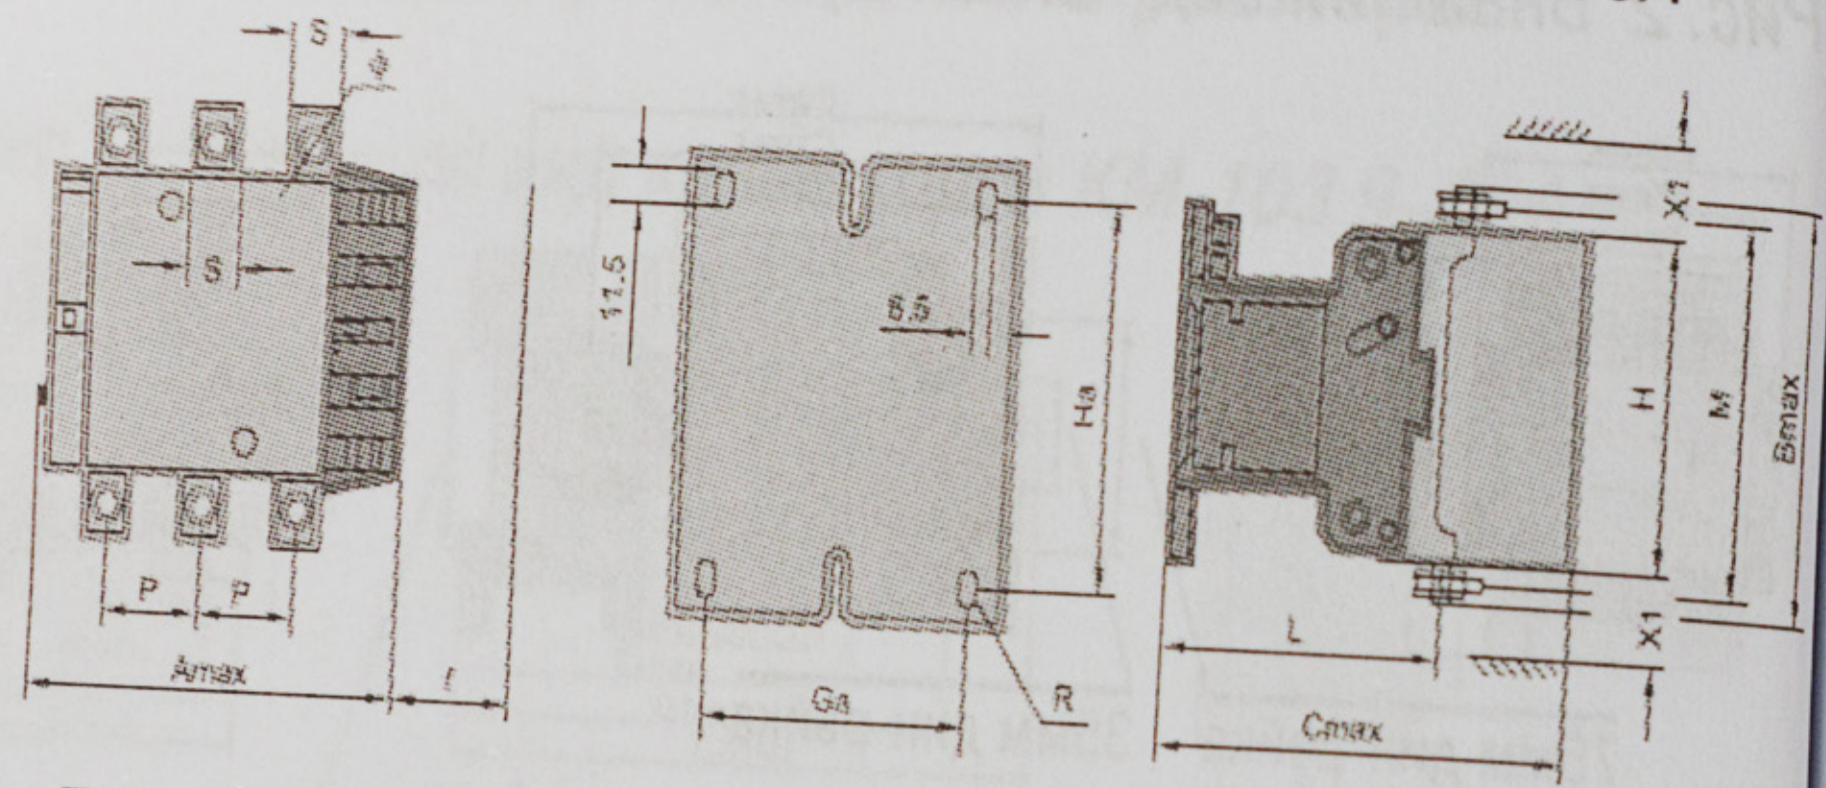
Внешний вид контакторов КМ-103 400-500А
